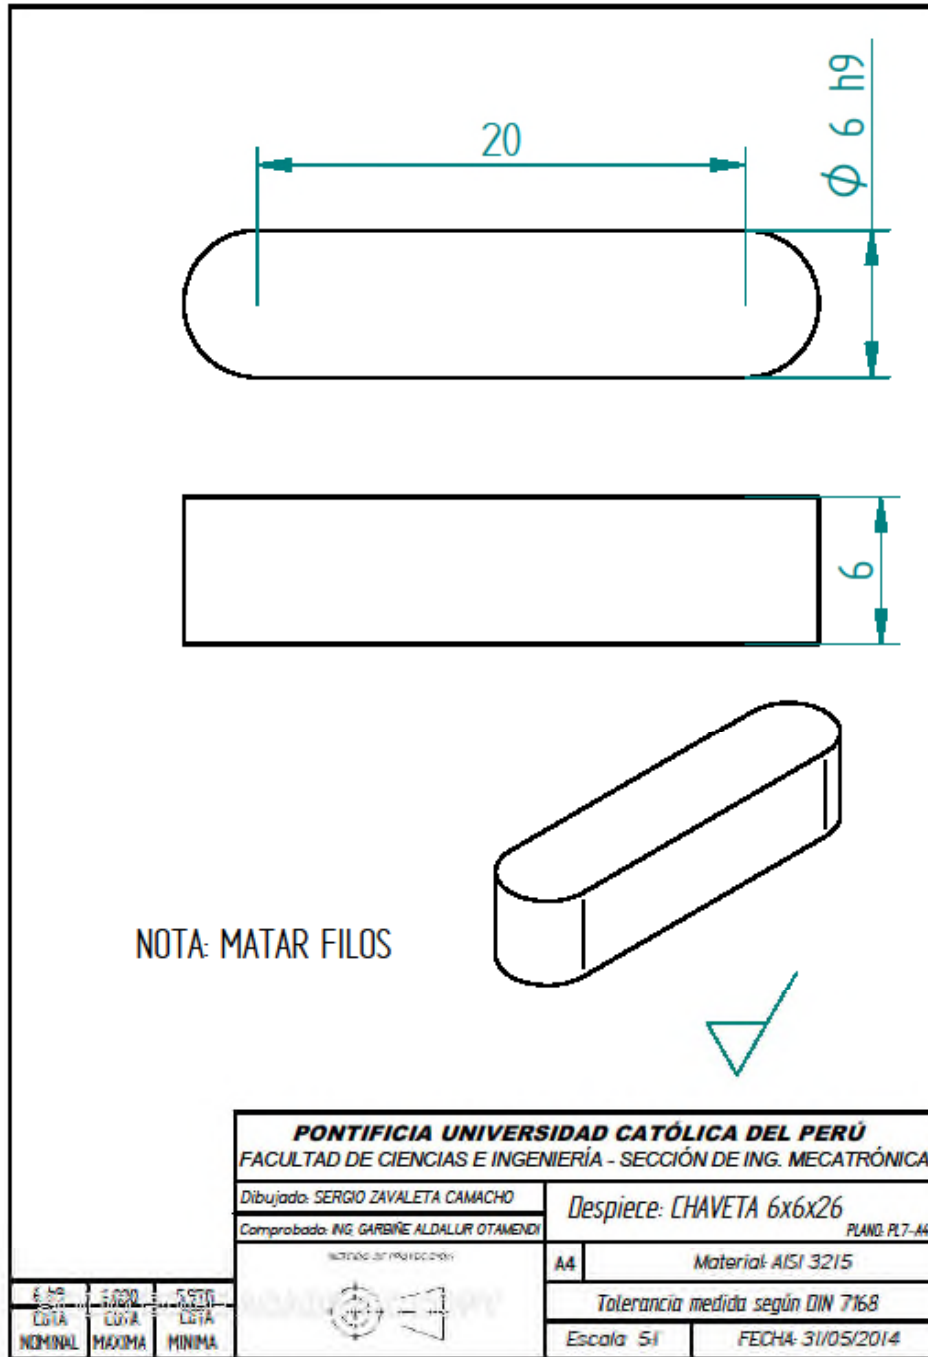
Plano de despiece de la chaveta del engranaje E2. Fuente: Elaboración propia.
